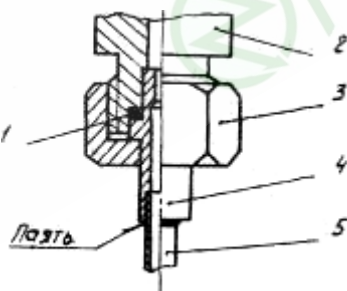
Подсоединение прибора к трубопроводу 1 — прокладка; 2 — штуцер; 3 — гайка; 4 — ниппель; 5 — трубопровод
